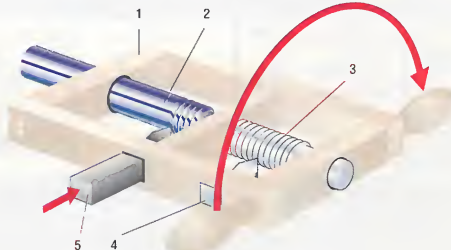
Копир Леонардо да Винчи для нарезания резьбы: 1 – рама; 2 – заготовка; 3 – эталонный винт (скреплен с заготовкой); 4 – штифт; 5 – резец.
